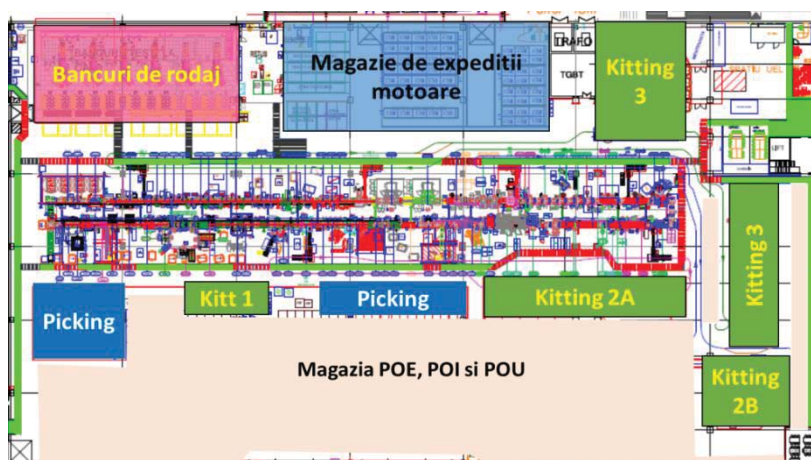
a. Reprezentarea zonelor de kitting în linia de asamblare motor H4
